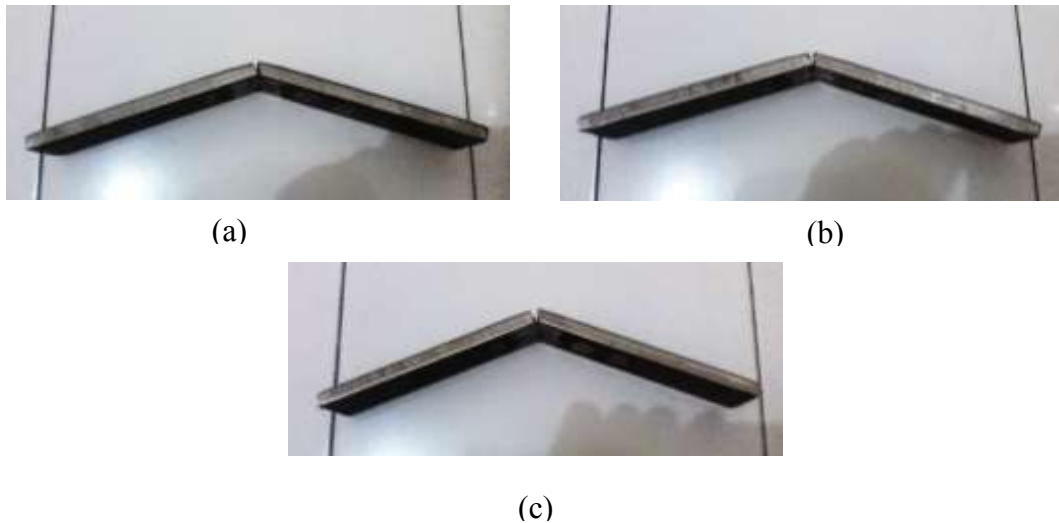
Hasil Uji *Face Bend* pengelasan SMAW di Darat; (a) sampe B1; (b) sample B2; (3) sample B3.
